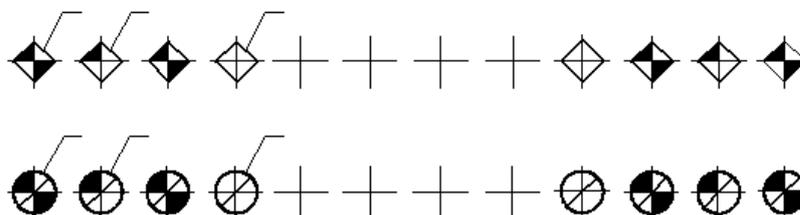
Изображение на сборочном чертеже групп крепежных деталей
